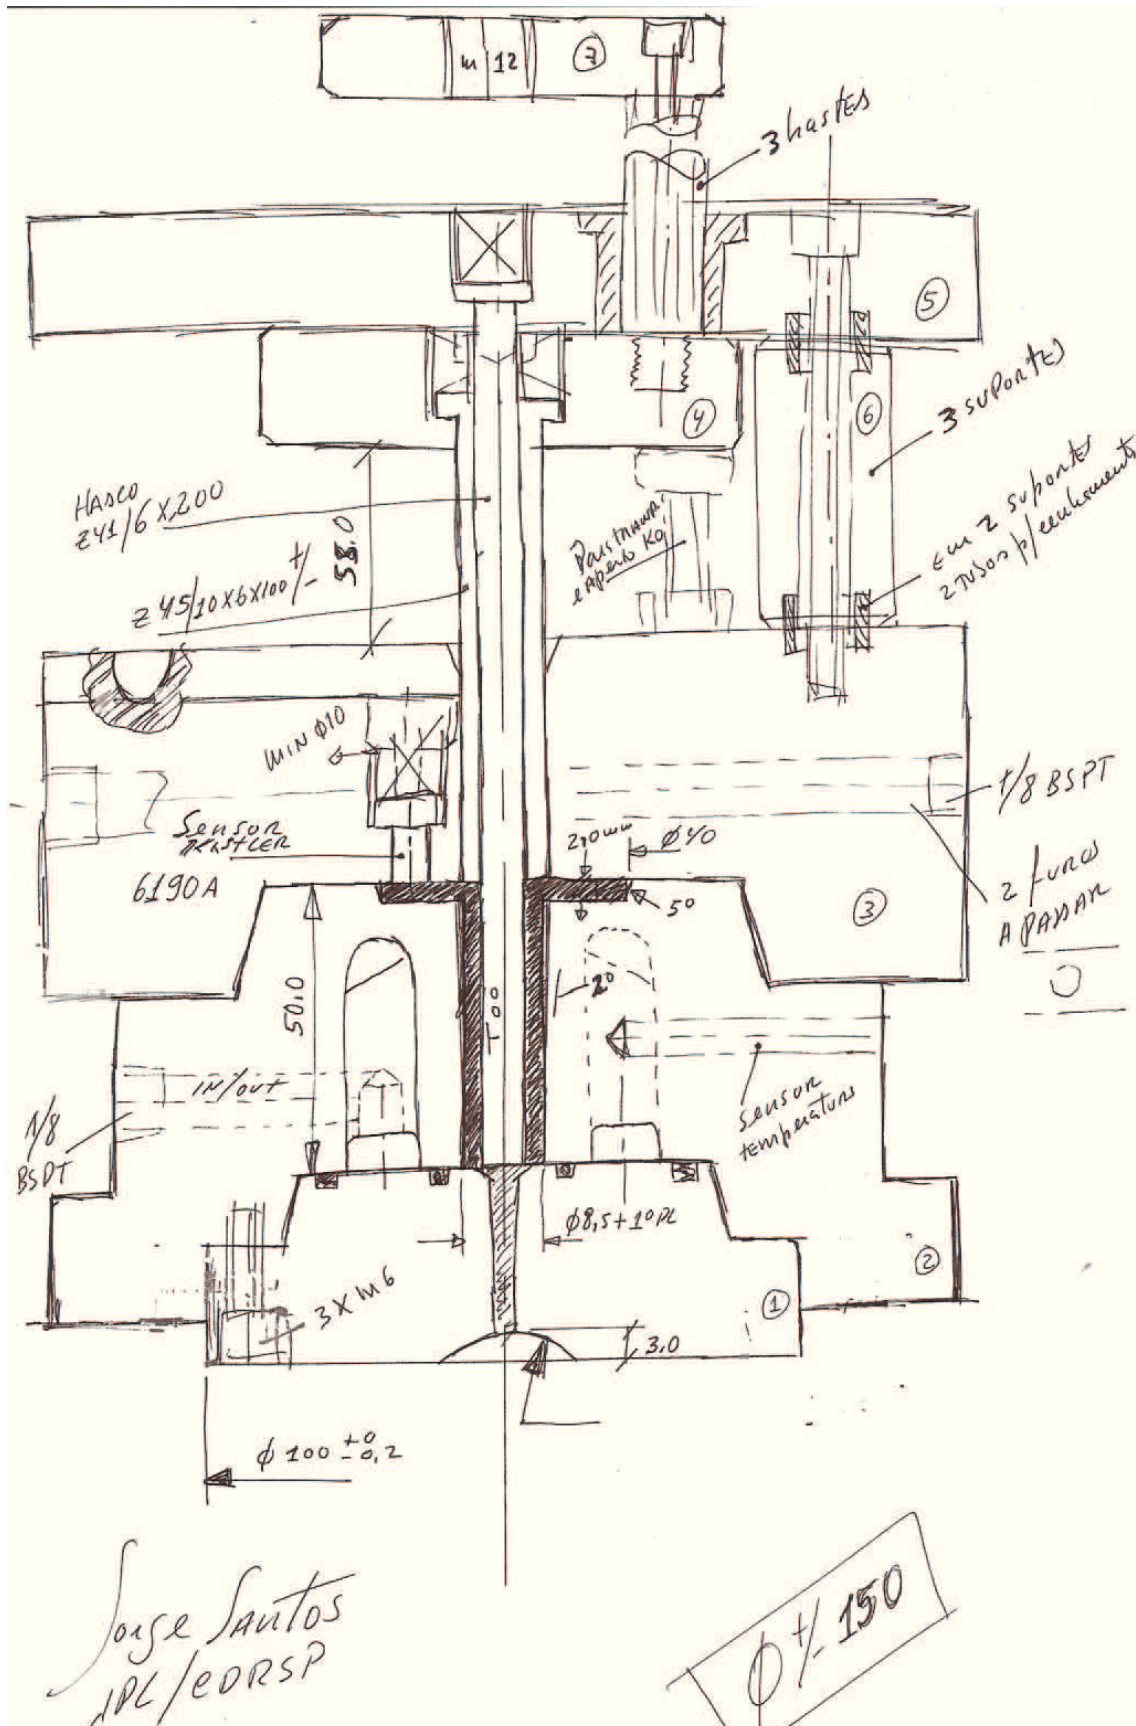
Esboço de molde protótipo para a realização de testes com revestimentos nos elementos moldantes.
